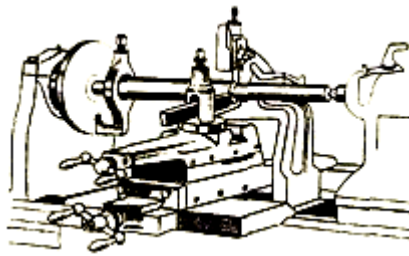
Обробка вала на токарному верстаті в центрах з використанням рухомого лонета
